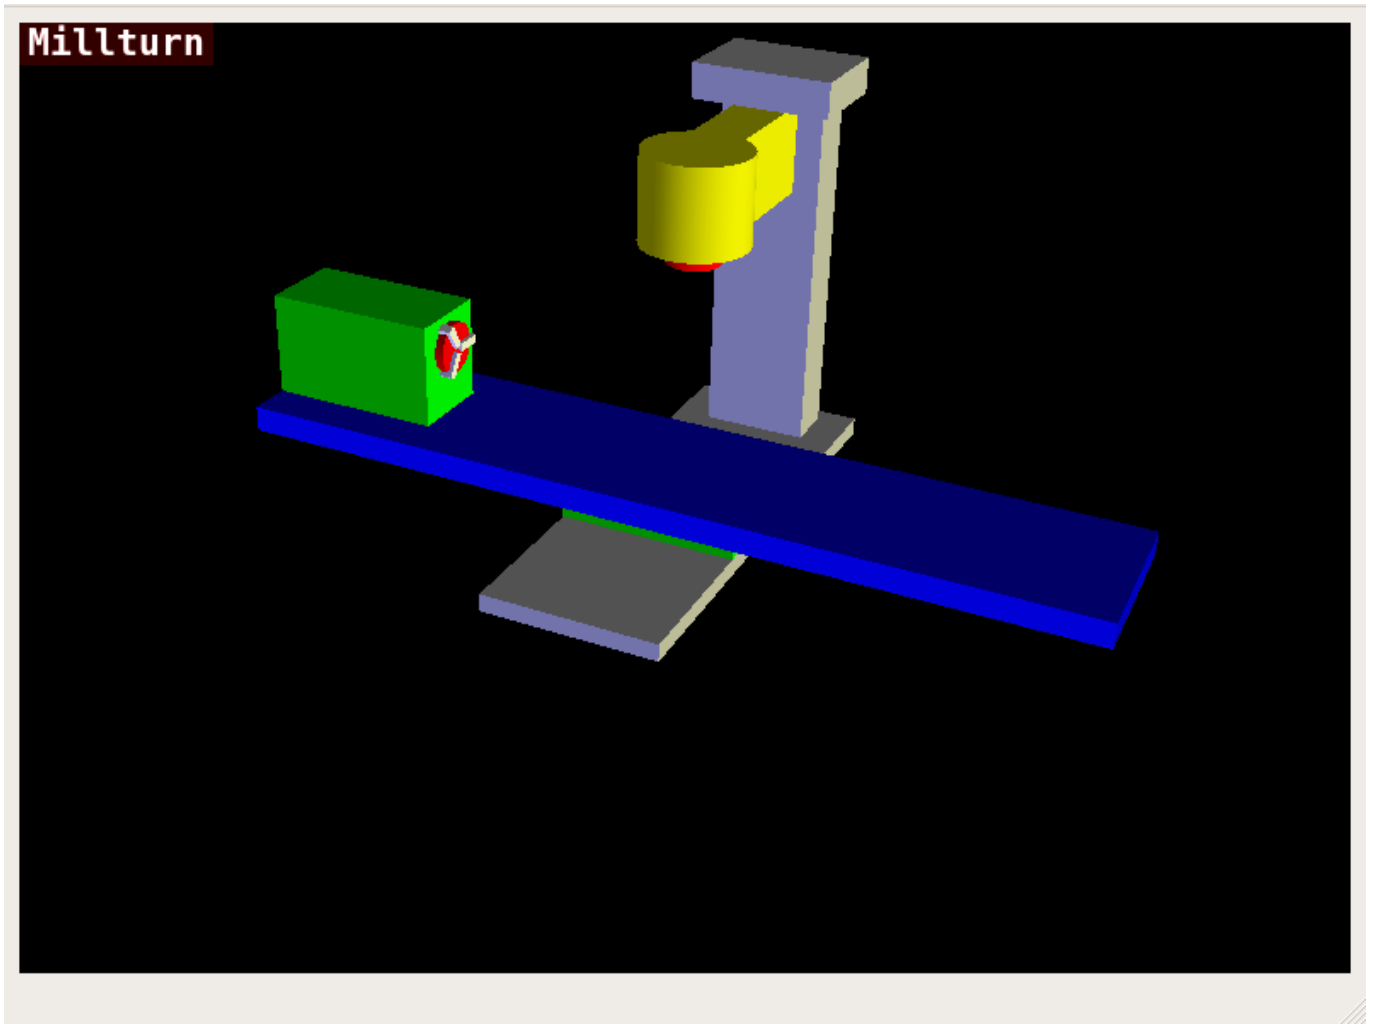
QtVCP `vismach_millturn` - Панель 3D-вигляду 4-осьового фрезерування/токарного верстата
